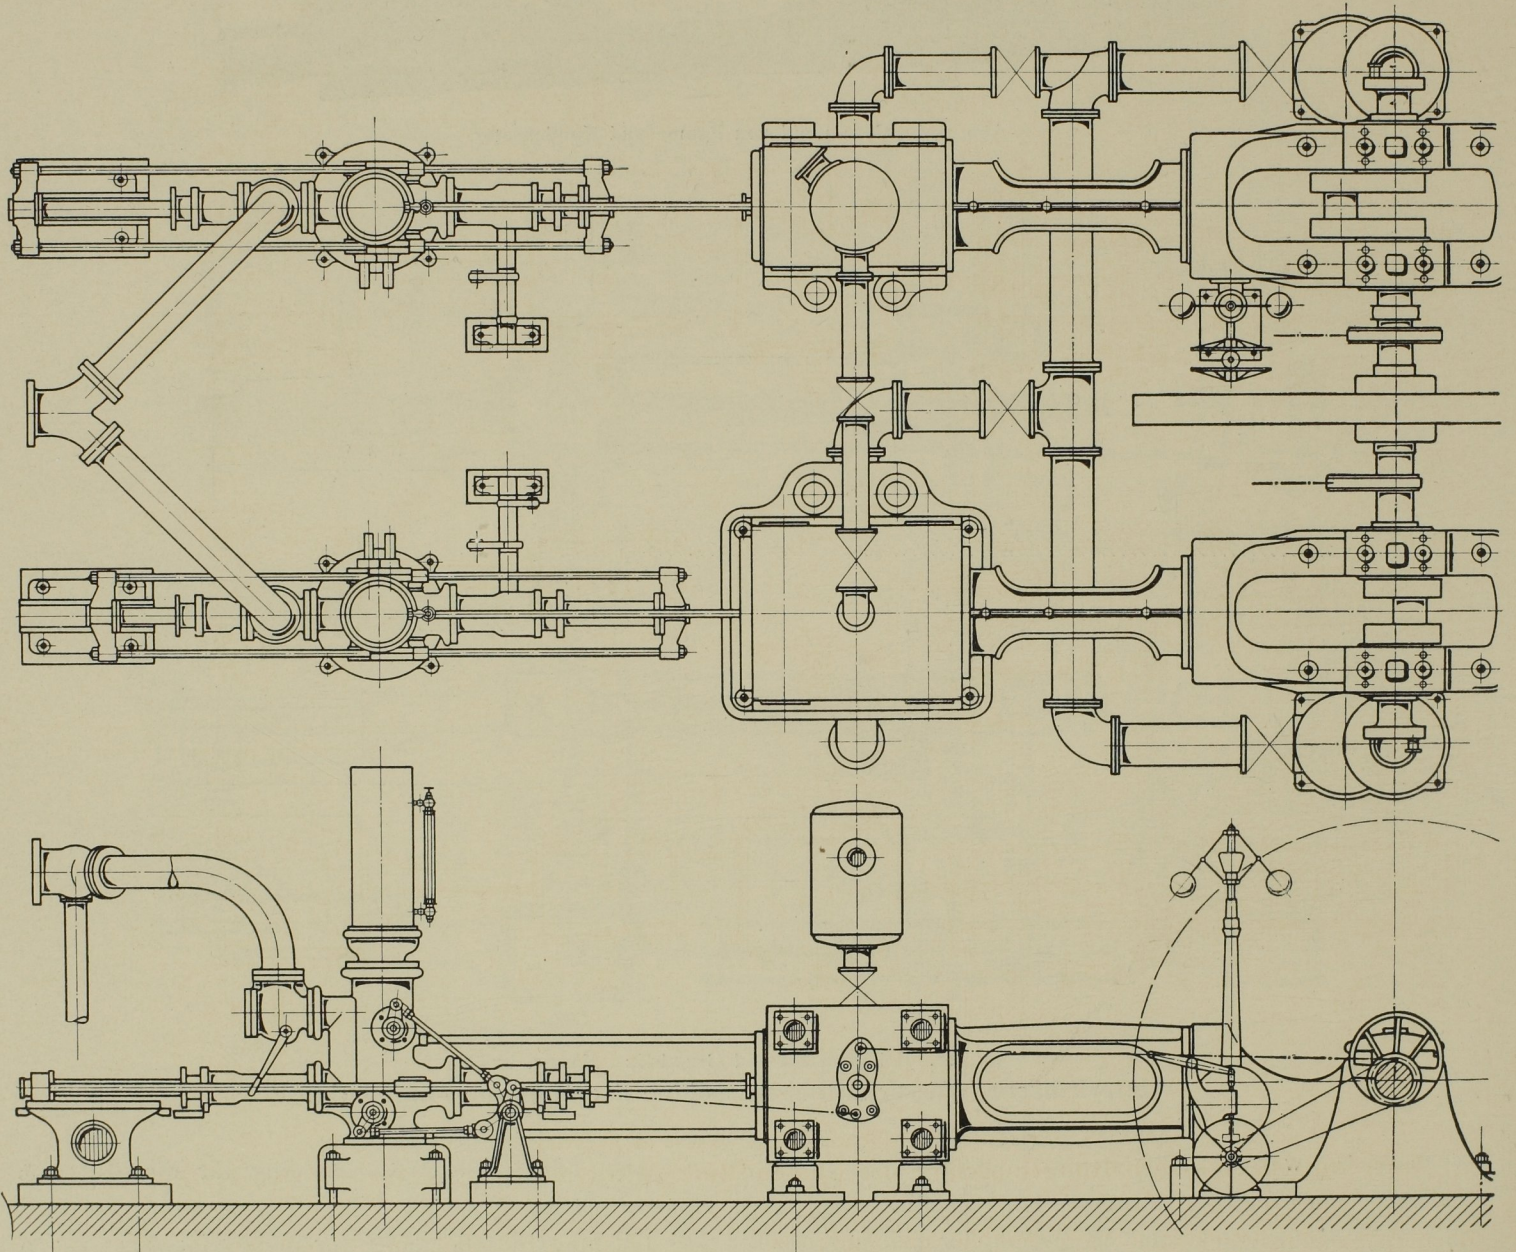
Grundriss und Seitenansicht. Masst. 1:48.
